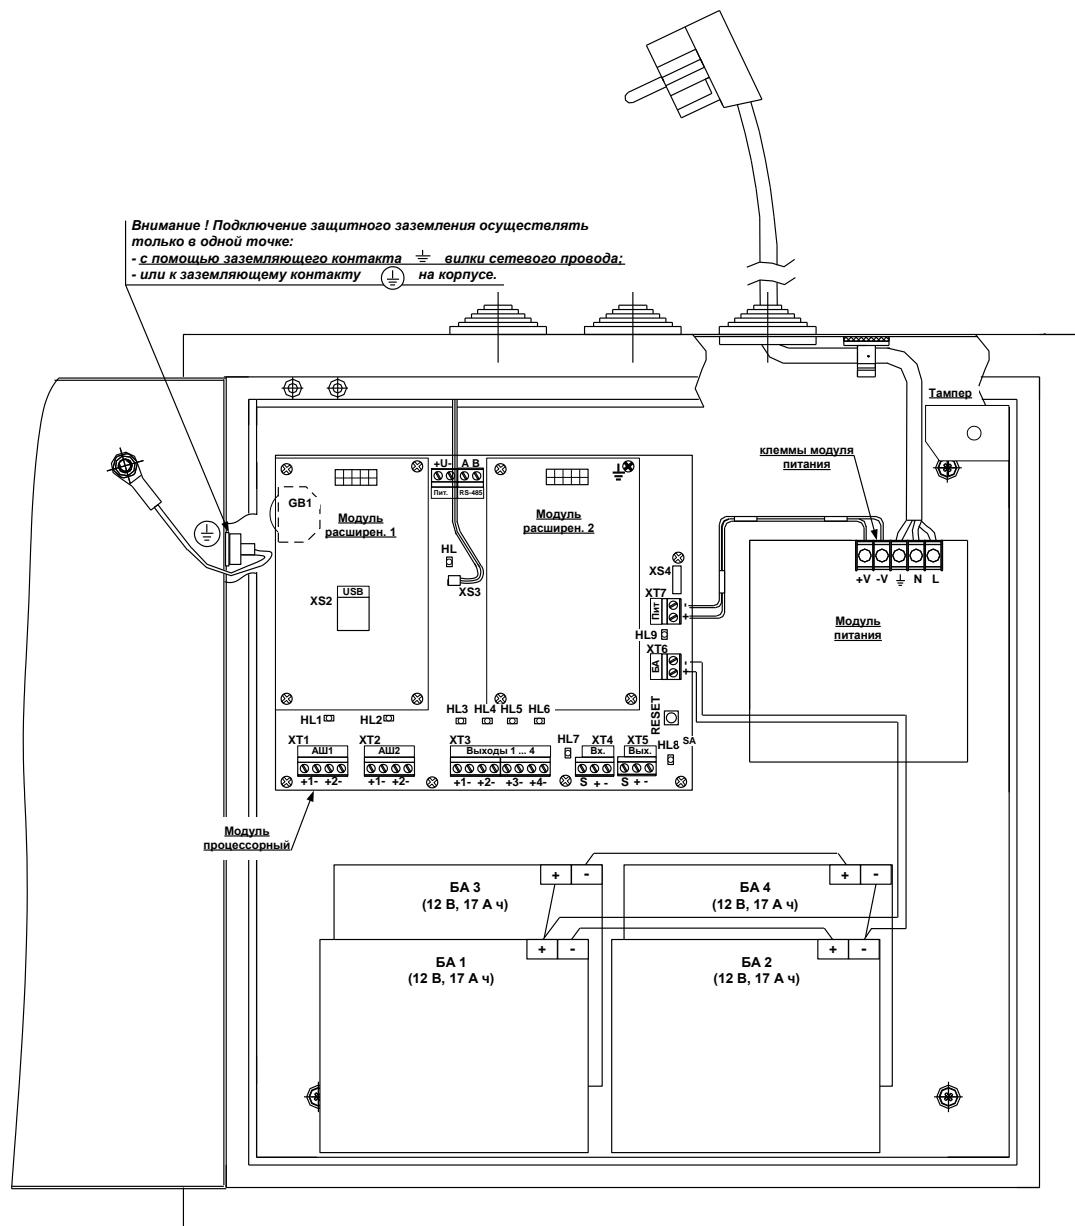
Внешний вид ППК-Р. Габаритные и присоединительные размеры
